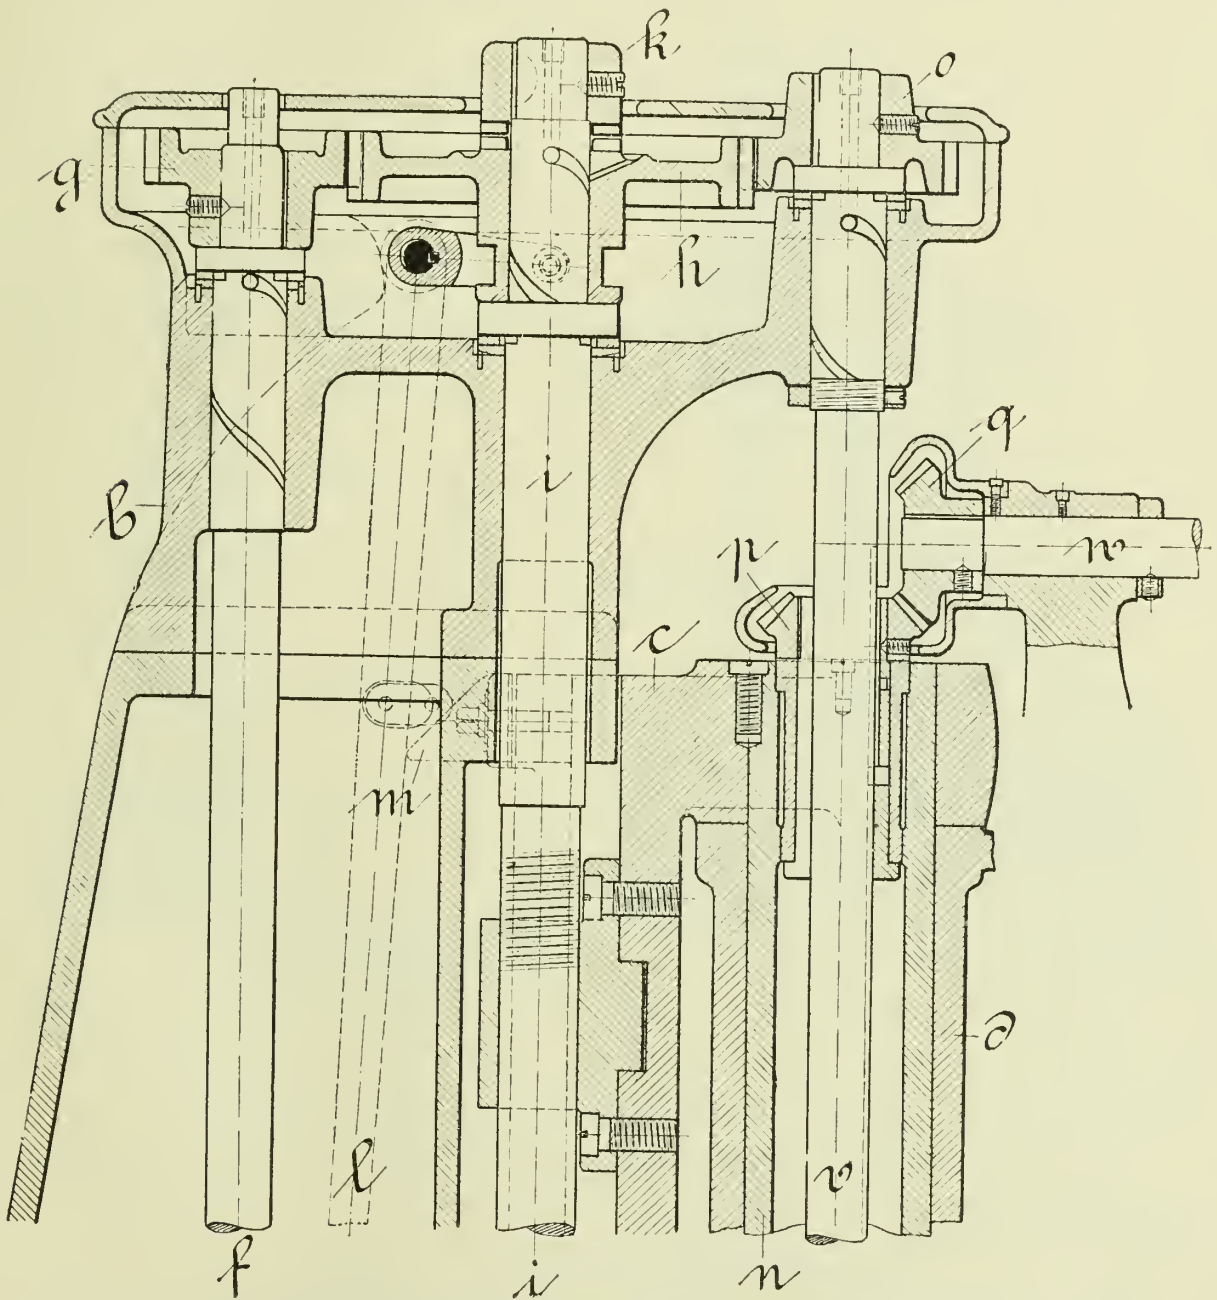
a. Kopf des Ständers der Radialbohrmaschine.
